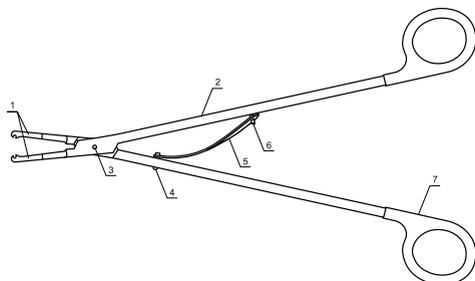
Внешний вид клипаппликатора многоразового нестерильного для открытой хирургии VOLKMANN для полимерных клипс: 1 – Бранши для захвата полимерных клипс; 2 – Рукоятка; 3 – Винт; 4 – Заклепка; 5 – Пластинчатая пружина; 6 – Крючок; 7 – Насадка на кольца рукоятки.
